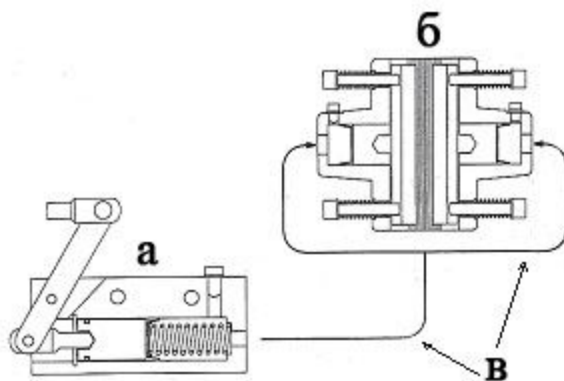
а) Главный тормозной цилиндр б) Суппорт тормозов в) Дюритовые шланги.
